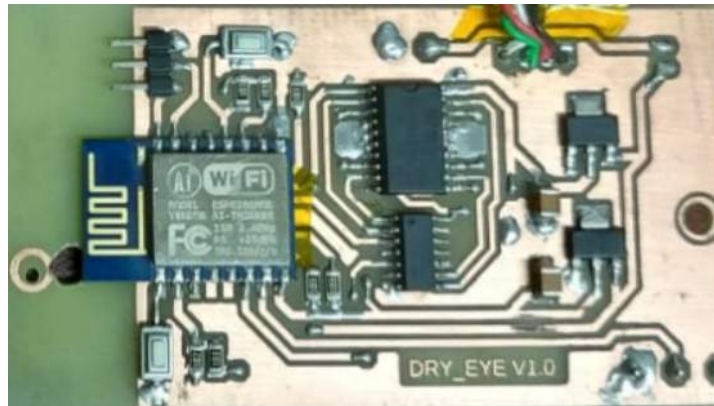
Construcción de la placa PCB acabado con componentes.
